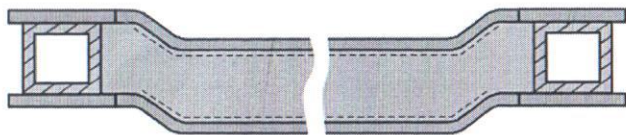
Контроль околошовной зоны сварного соединения соединения боковых стенок с верхним и нижним листами поперечных балок
